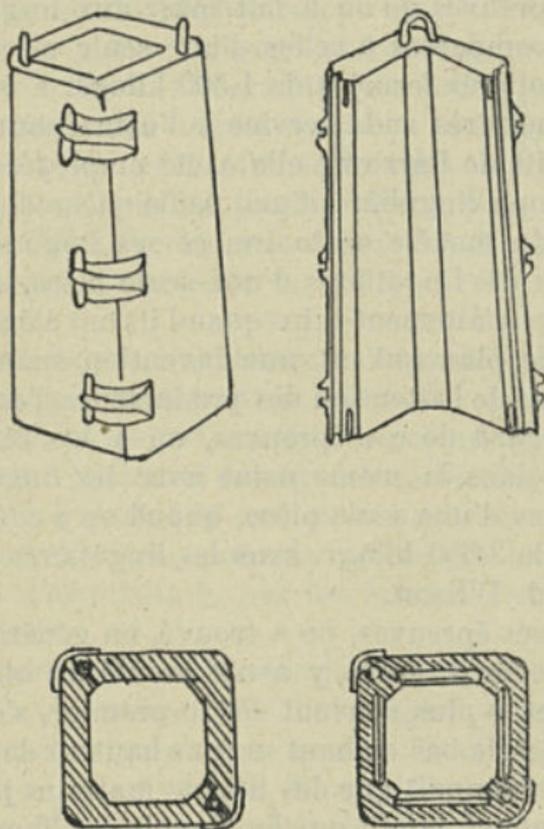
et 273. Lingotières ouvertes Wilson, pour acier Bessemer.
